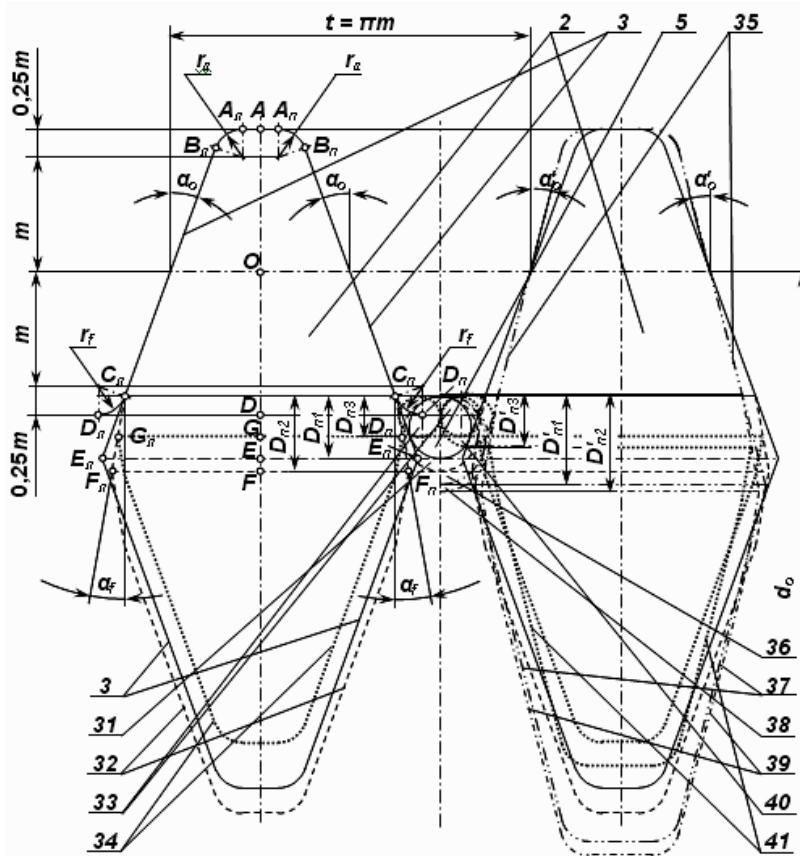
Профили предлагаемых режущих пластин и варианты размещения между их боковыми поверхностями крепежных пружин
